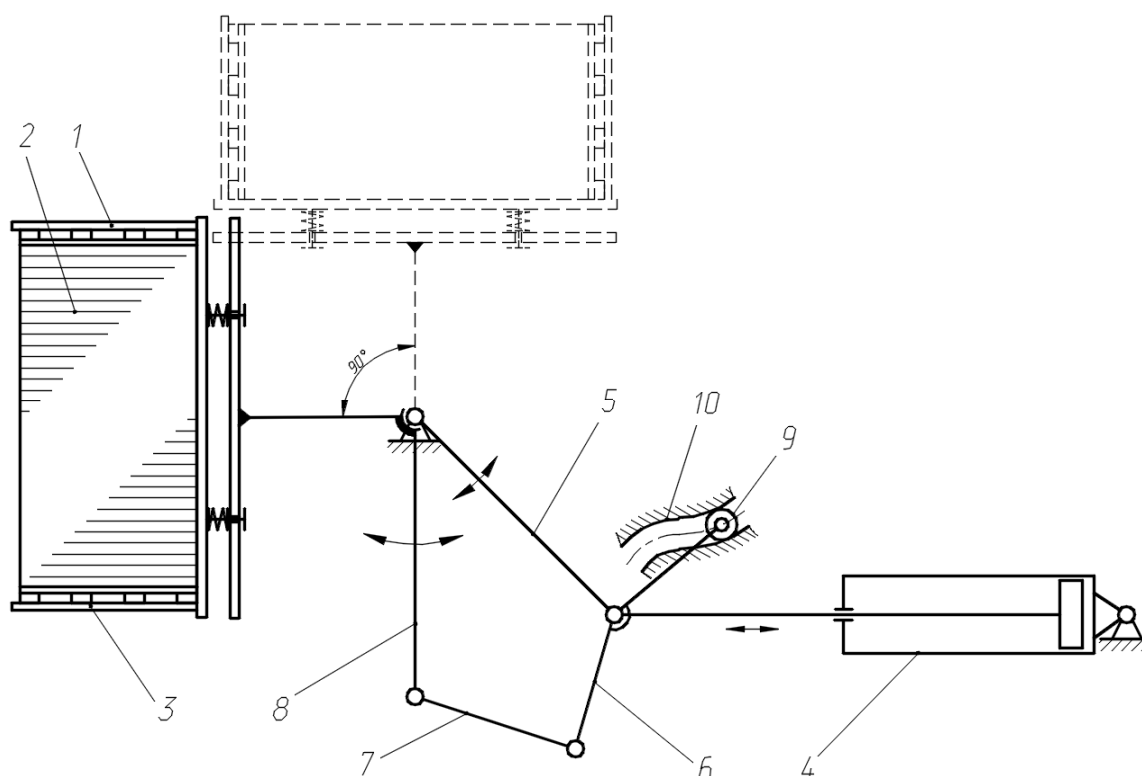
Принципова схема пристрою повертання транспортного пакету на 90°
